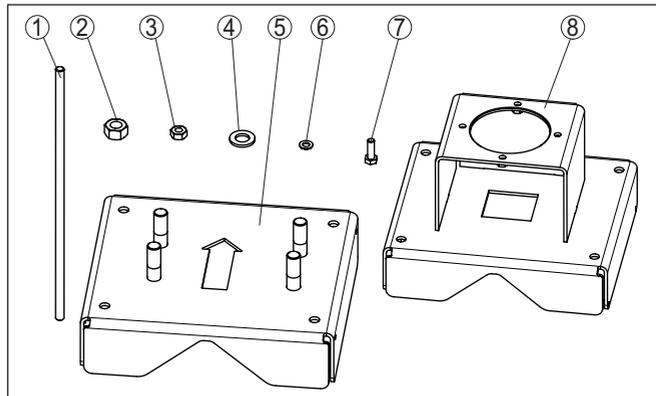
Dispositif de fixation pour conduites traversées perpendiculairement KV 31, Montage horizontal du capteur
